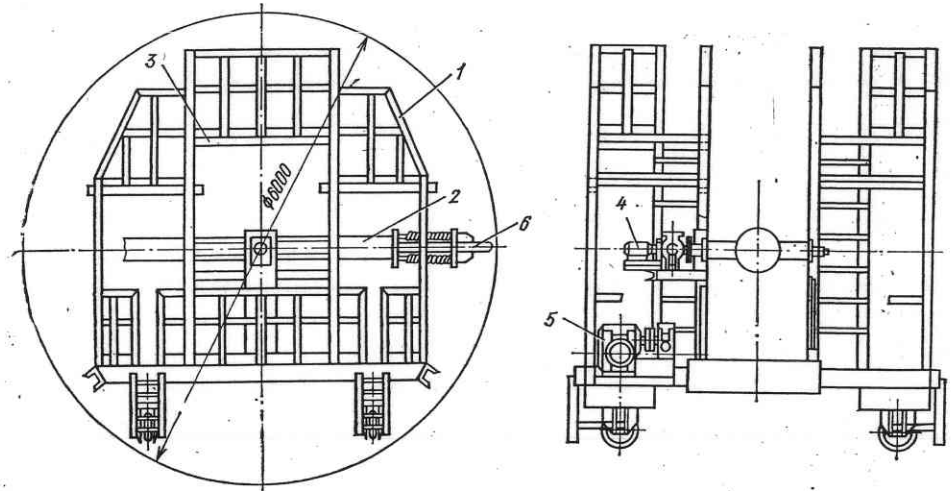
Передвижное распорное устройство с механизированным приводом:
